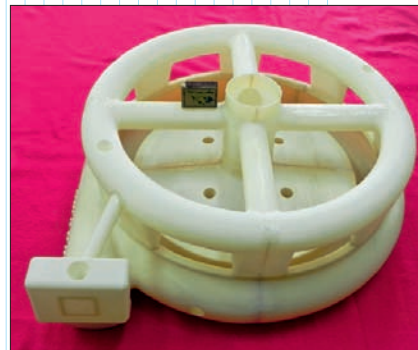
Модель корпуса с элементами ЛПС, изготовленная из 12-ти частей
